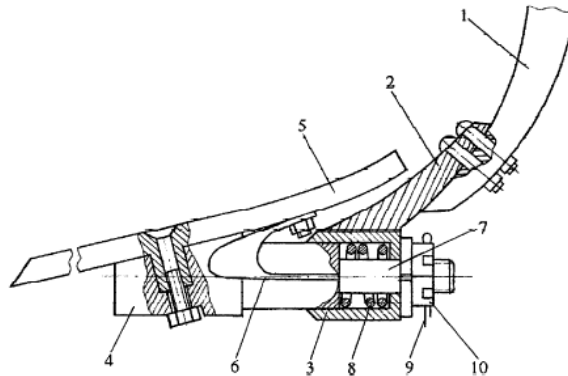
Лапа культиватора: 1 – стійка; 2 – наральник; 3 – стакан; 4 – стрижень; 5 – лапа; 6 – пружний елемент; 7 – задня частина стрижня; 8 – пружина; 9 – шплінт; 10 – корончаста гайка.
